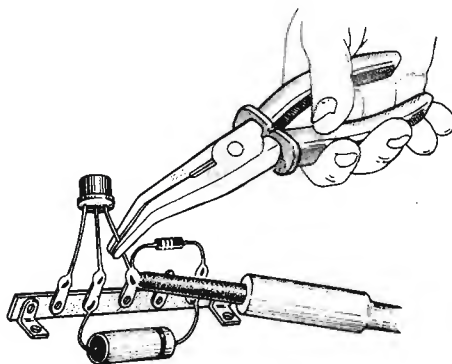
Quando si salda un terminale di un transistor occorre sempre impedire che il calore del saldatore raggiunga la massa del transistor stesso. Si risolve facilmente questo importante problema stringendo il terminale fra i becchi di una pinza metallica.
